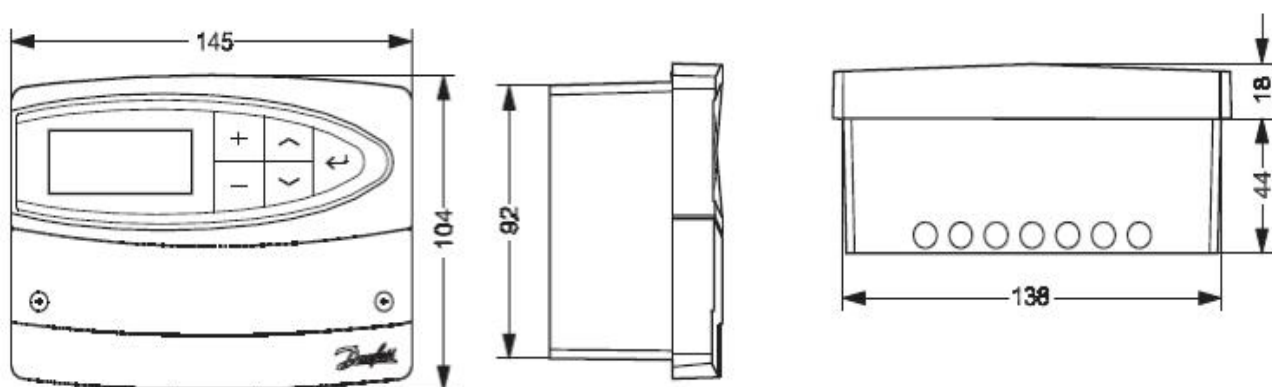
Габаритные и присоединительные размеры ECL Comfort 110.
